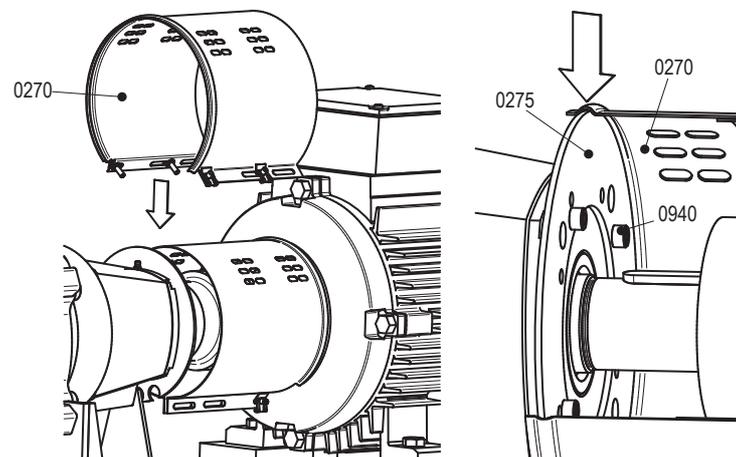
Montieren der Haube auf der Pumpenseite.
